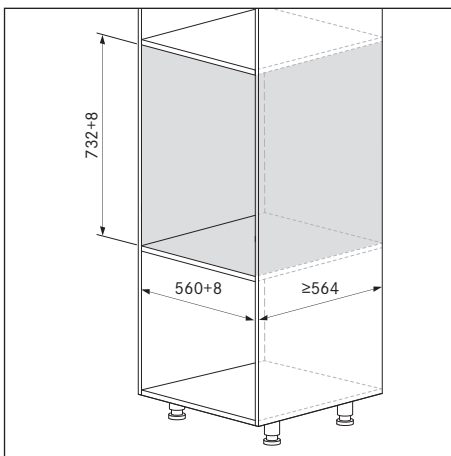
Dimensões de montagem MS140/MSS140 + X BO
